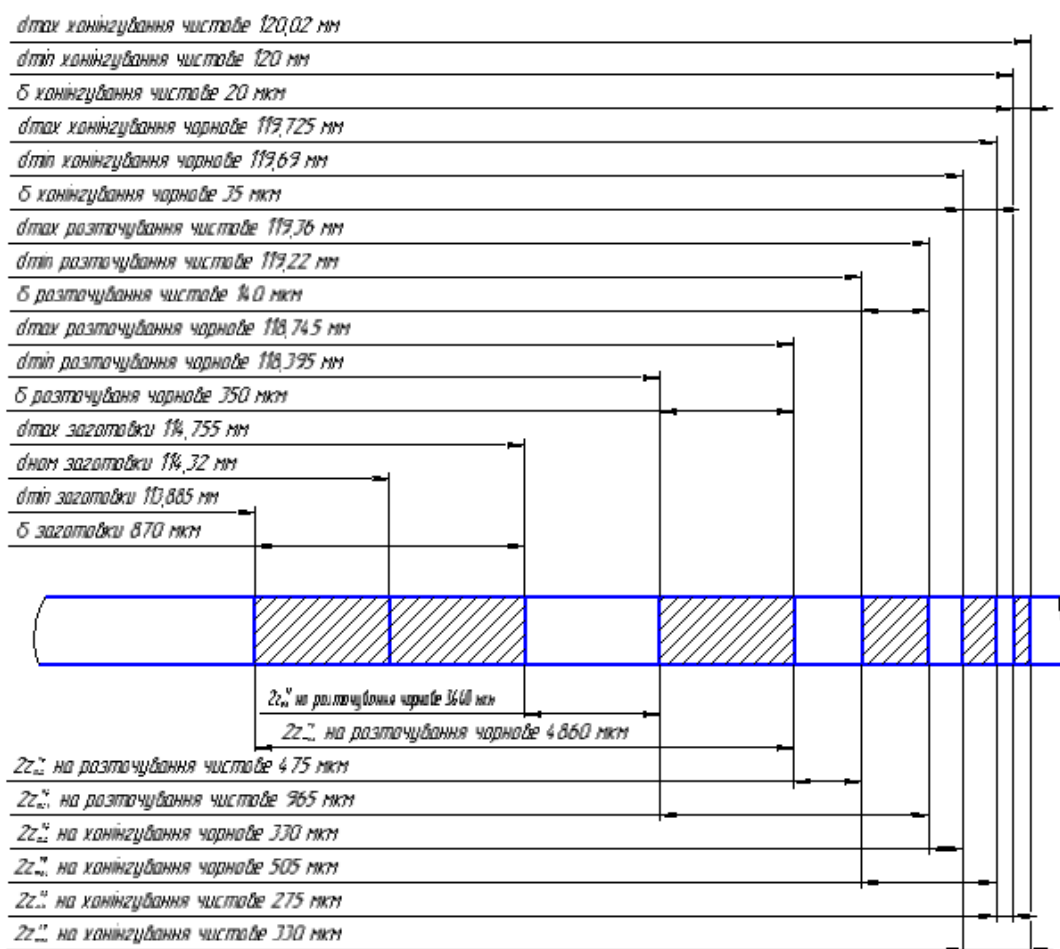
Схема розташування припусків та допусків
